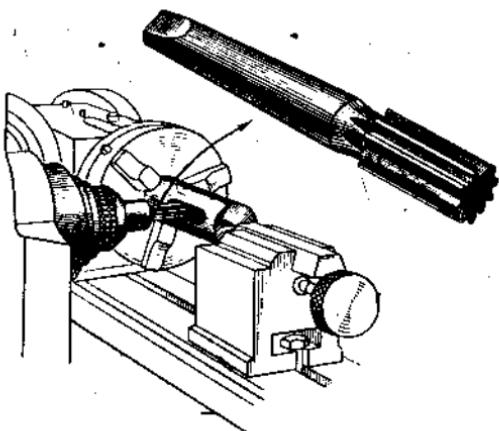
Фрезерование шпоночного паза на валу для закладной шпонки.
